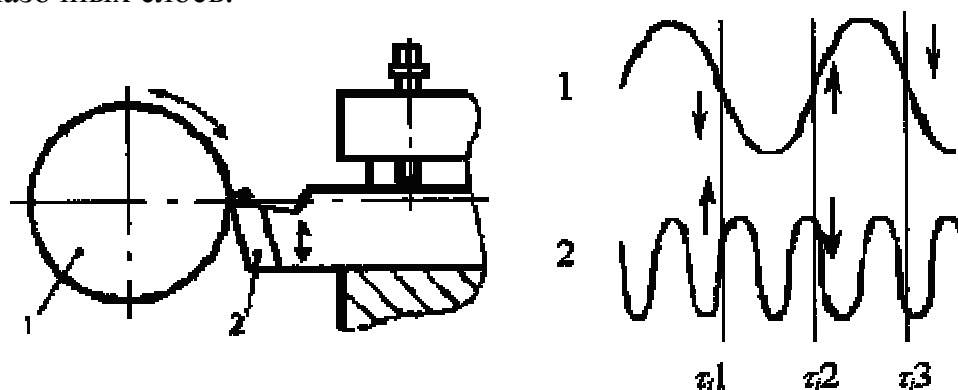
5. Схема колебательных движений заготовки 1 и режущего инструмента 2 в процессе резания.
